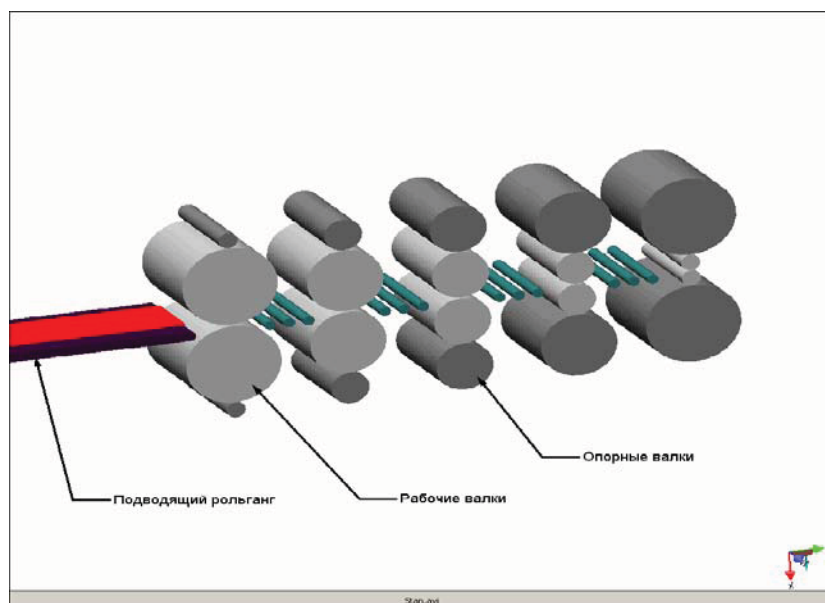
Общий вид непрерывного стана для прокатки тонких полос
